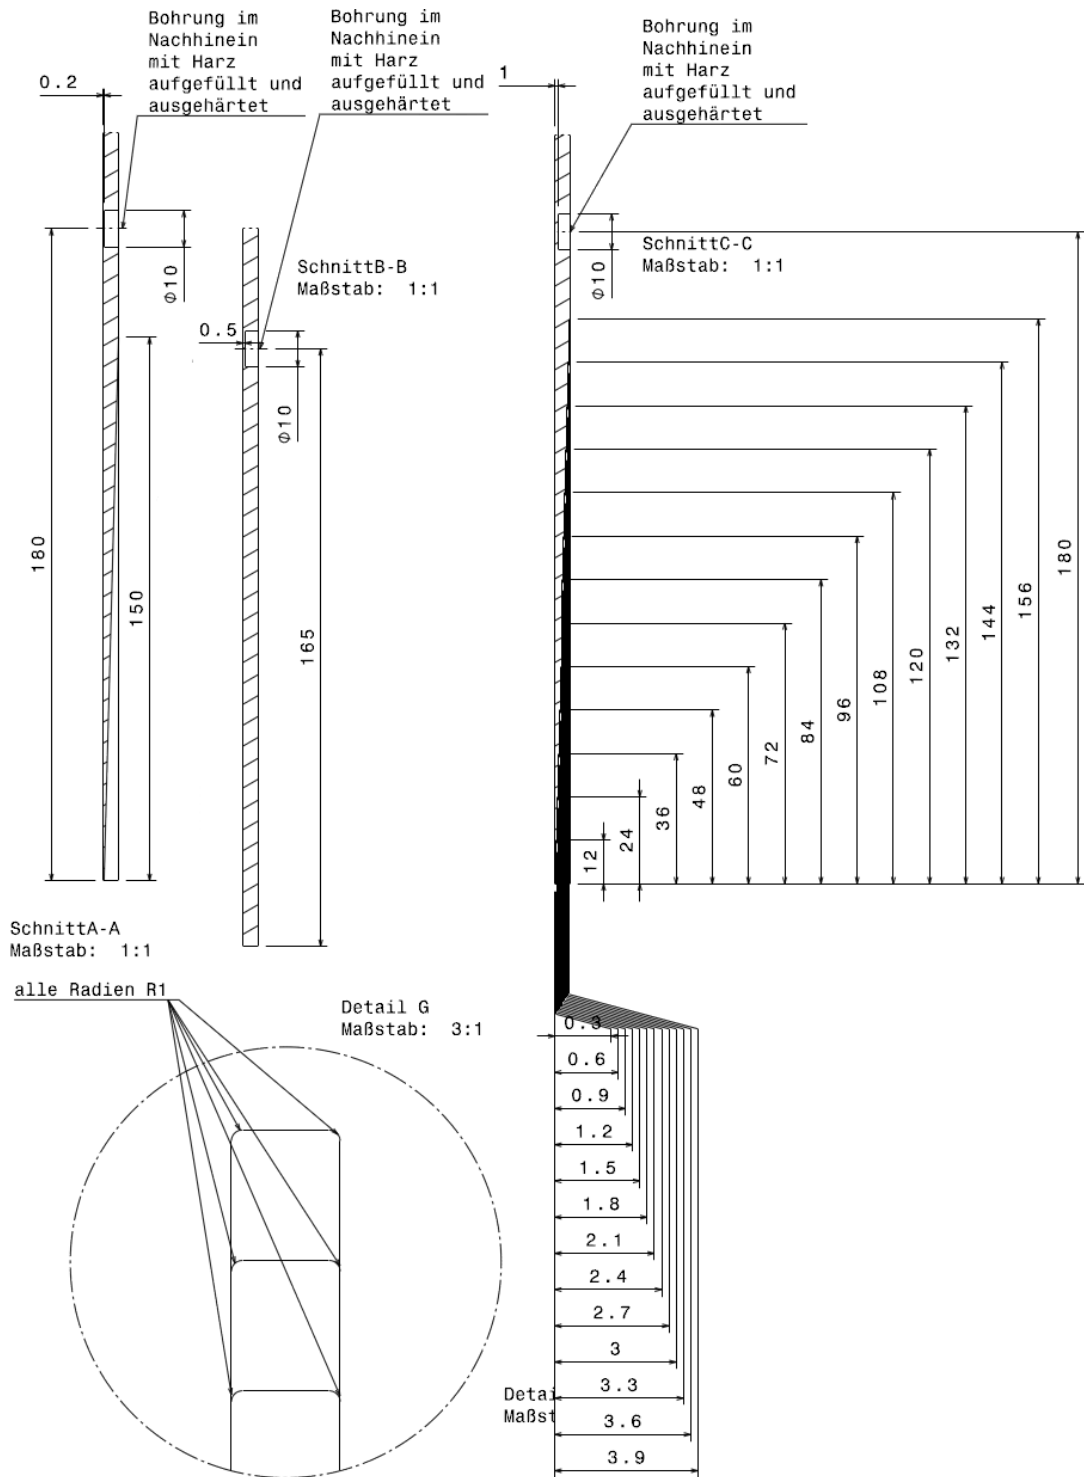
Mechanische Bearbeitung: Schnitte I
